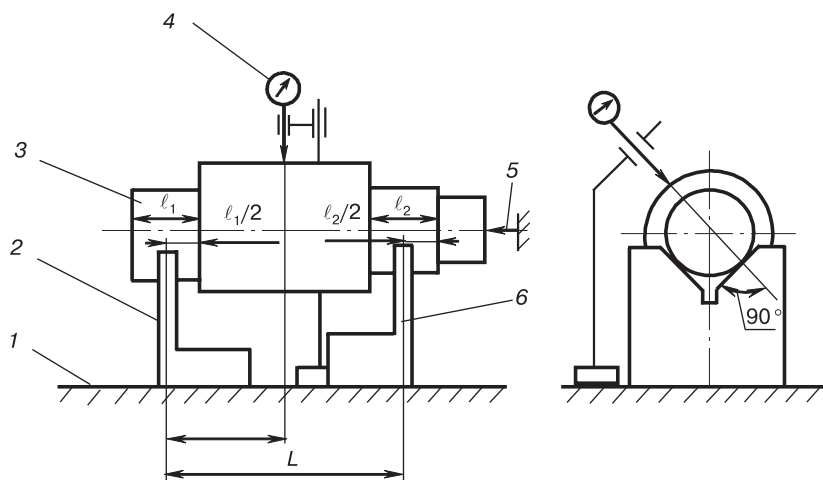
Схема измерения радиального биения наружной поверхности шлиц относительно общей оси шеек под подшипники:
